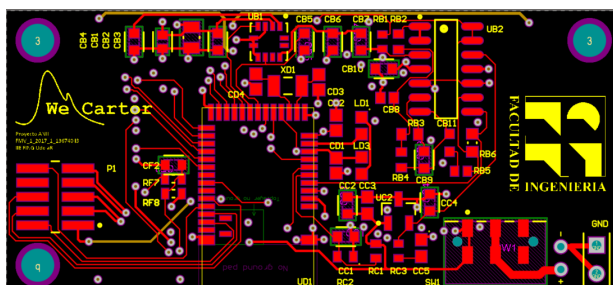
Layout de la PCB final del dispositivo vestible. Solo capa superior (TOP) visible. Las dimensiones de la PCB son $55\text{mm} \times 25\text{mm}$. Esta capa contiene al canal BCG del AFE y acelerómetro (arriba), parte del PMC del dispositivo y el módulo MDBT42Q (abajo). Además también dispone el conector de programación del microcontrolador (izquierda), el conector de batería y *switch* de encendido (derecha).
